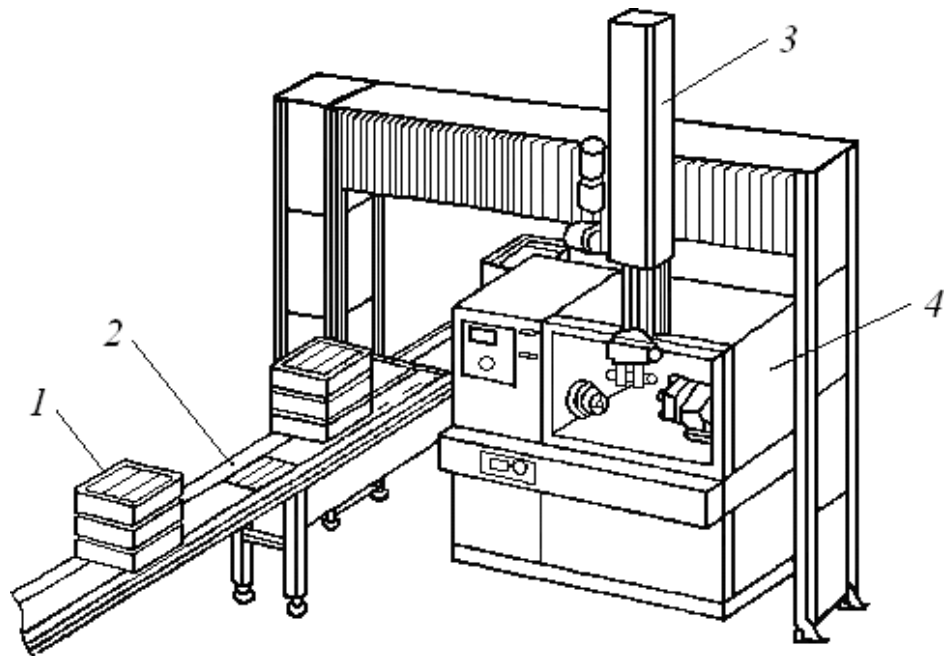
Загальний вигляд РТК для обробки деталей типу «тіла обертання» з обслуговуючим роботом порталного типу
